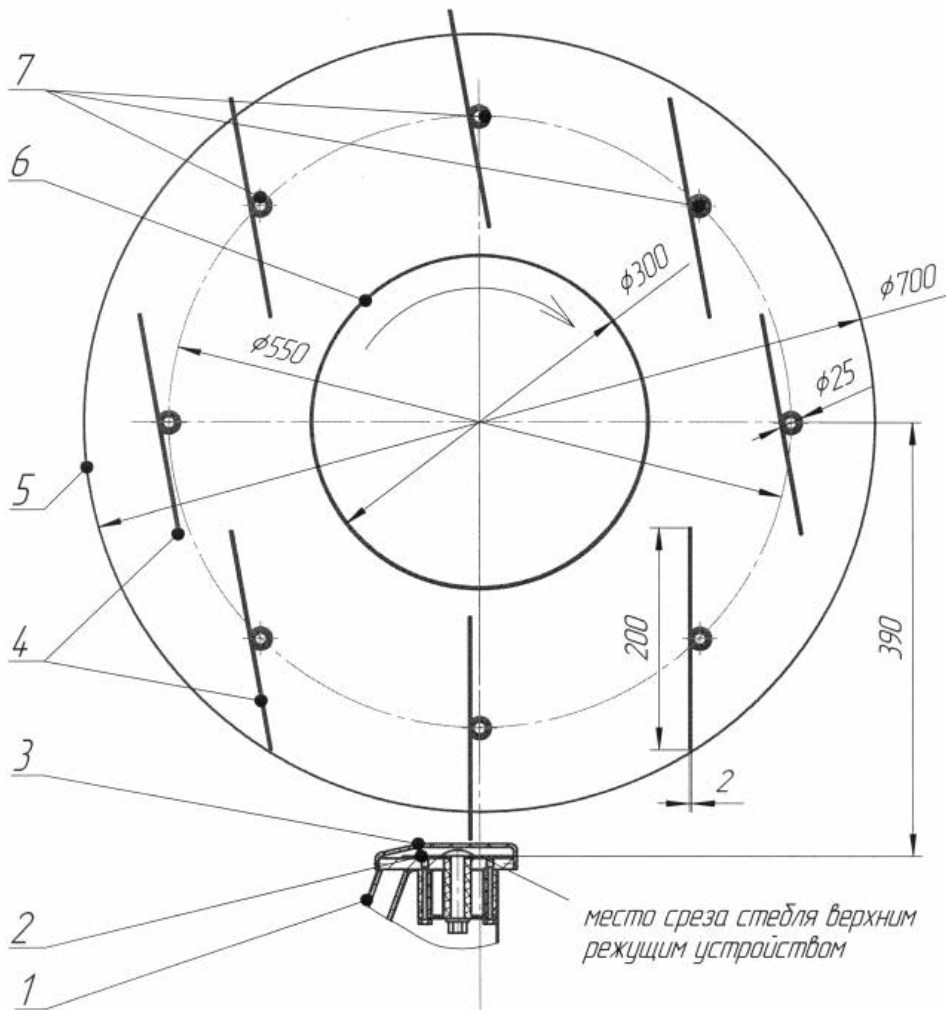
Поперечное сечение мотовила и его основные геометрические параметры: 1 – ковш; 2 – режущее устройство; 3 – защитный кожух; 4 – планка; 5 – боковой диск; 6 – вал; 7 – ось
